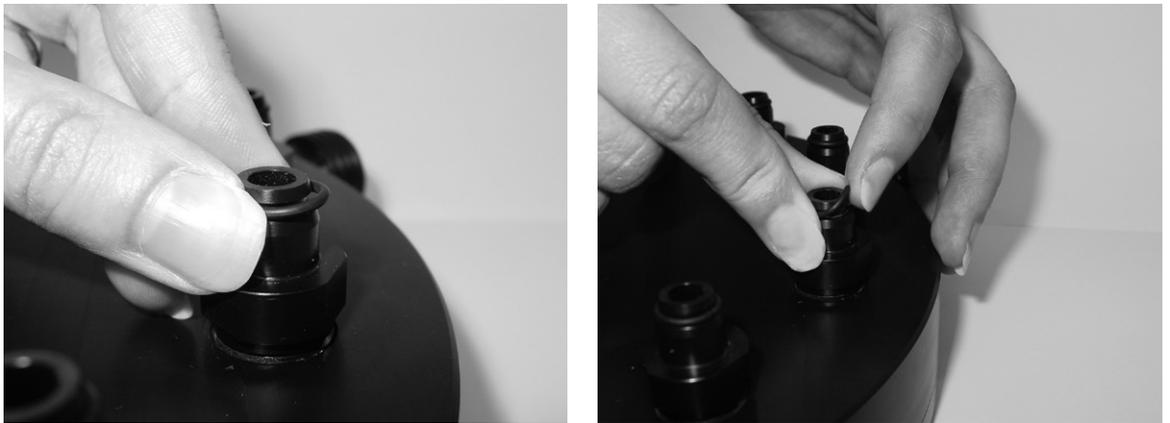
Remplacement des joints toriques des adaptateurs coniques
